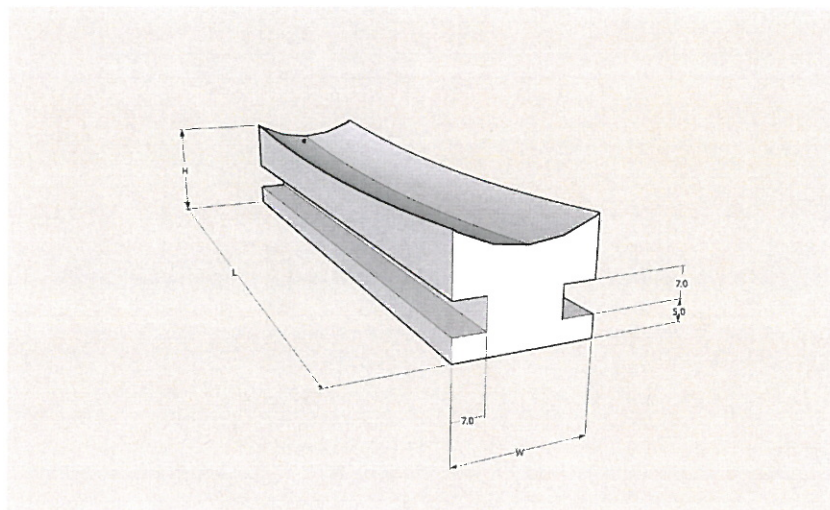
Dimensioni degli specchi (in mm) ed alloggiamenti per il supporto meccanico nel caso di specchi con H=25mm.
